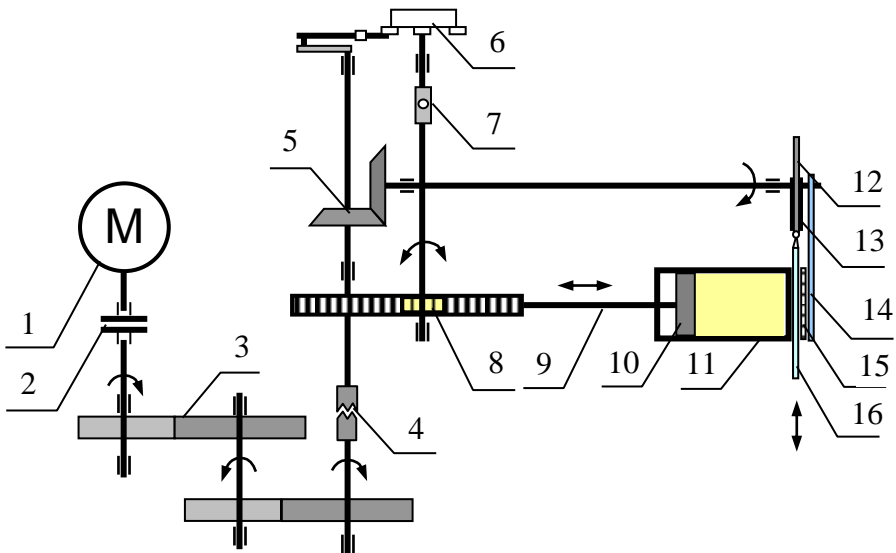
Кінематична схема шпигорізки: 1 – електродвигун; 2 – пружна муфта; 3 – циліндрична зубчаста передача; 4 – запобіжна муфта; 5 – конічна зубчаста передача; 6 – механізм циклічного переміщення поршня; 7 – механізм включення; 8 – рейкова передача; 9 – шток; 10 – поршень; 11 – короб; 12 – повідець; 13 – ексцентрик; 14 – серпоподібний ніж; 15, 16 – ножові рамки
